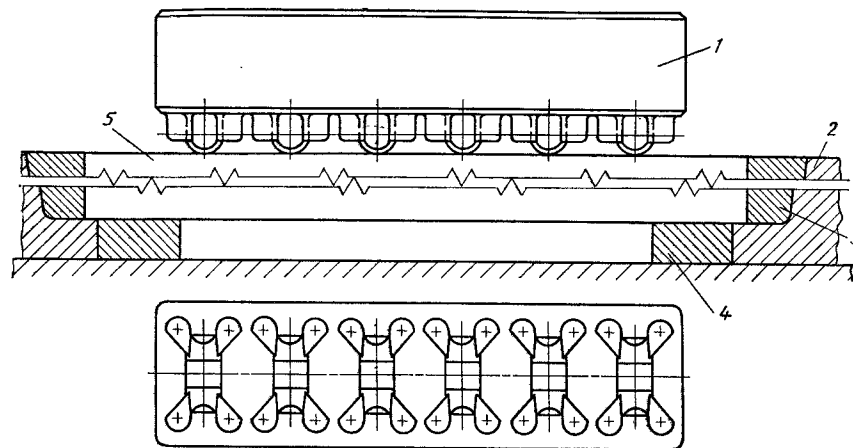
Пакет-штамп для выдавливания полостей пресс-форм и штампов в прямоугольных заготовках
